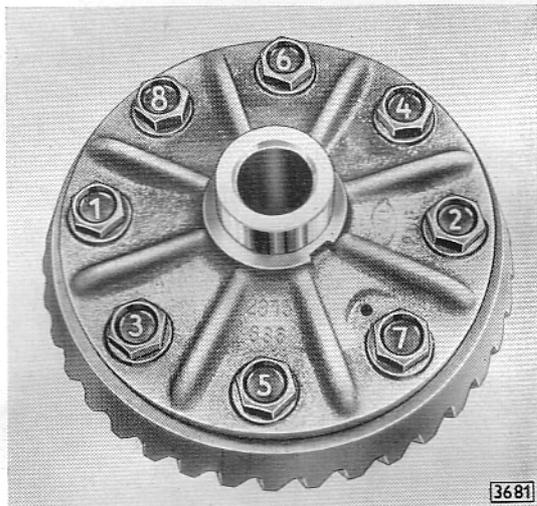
Reihenfolge für das Festziehen der Tellerradschrauben
